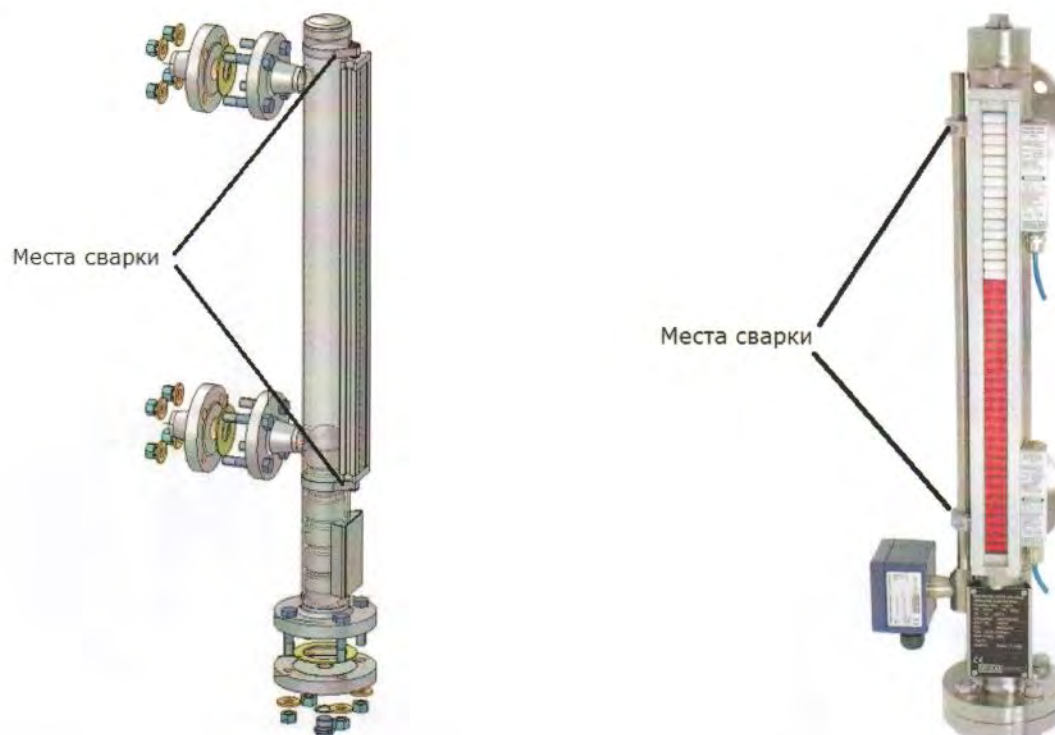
Места приварки корпуса датчика к корпусу уровнемера BNA
